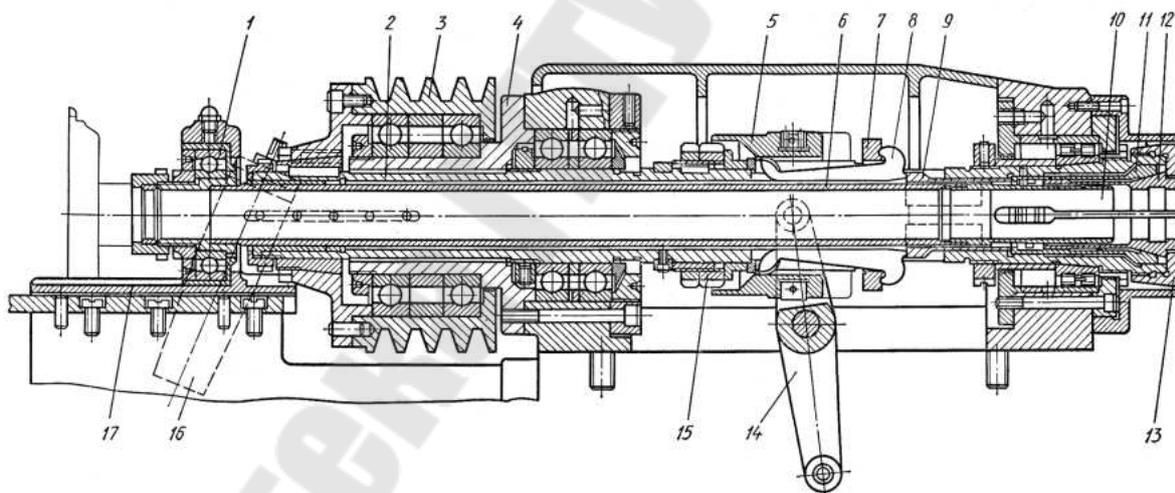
Шпиндельная бабка токарно-револьверного автомата 1Б140:
